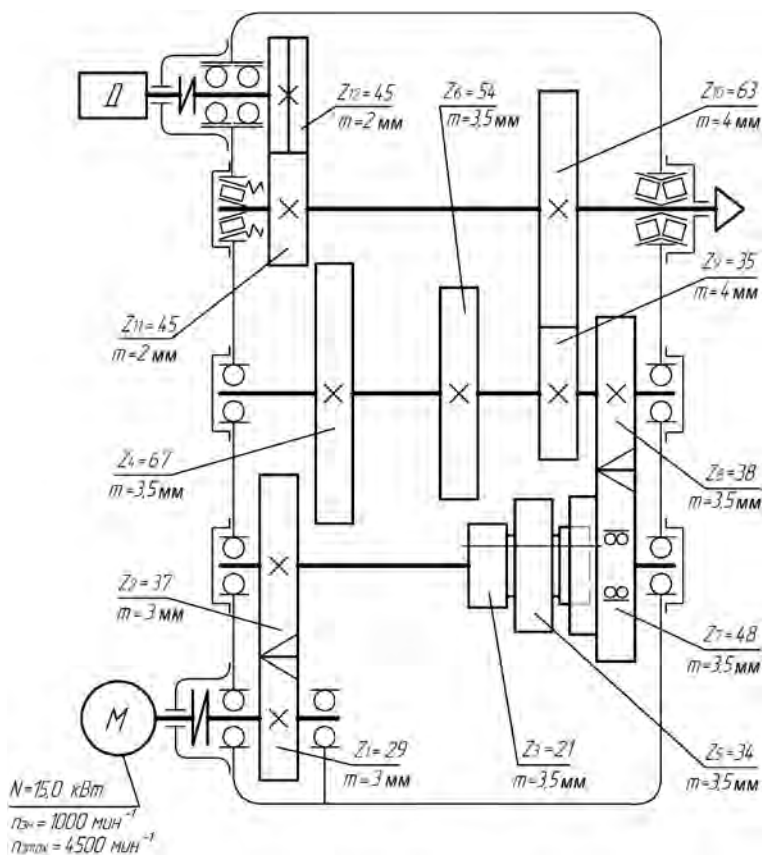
Кинематическая схема шпиндельной бабки горизонтального многоцелевого станка со встроенными в единый корпус шпиндельным узлом и коробкой скоростей
